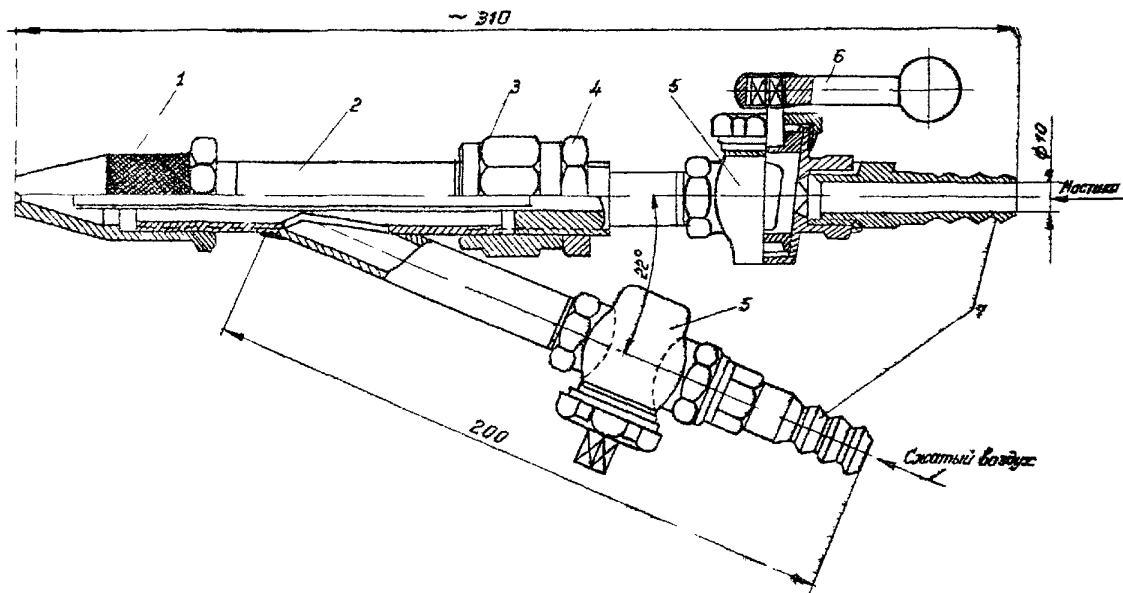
Схема форсунки для нанесения эпоксидно-дегтевого состава: 1- сопло; 2- двойник; 3- муфта; 4- контрайка; 5- ниппель; 6 - ручка; 7- ниппели (размеры в миллиметрах).
